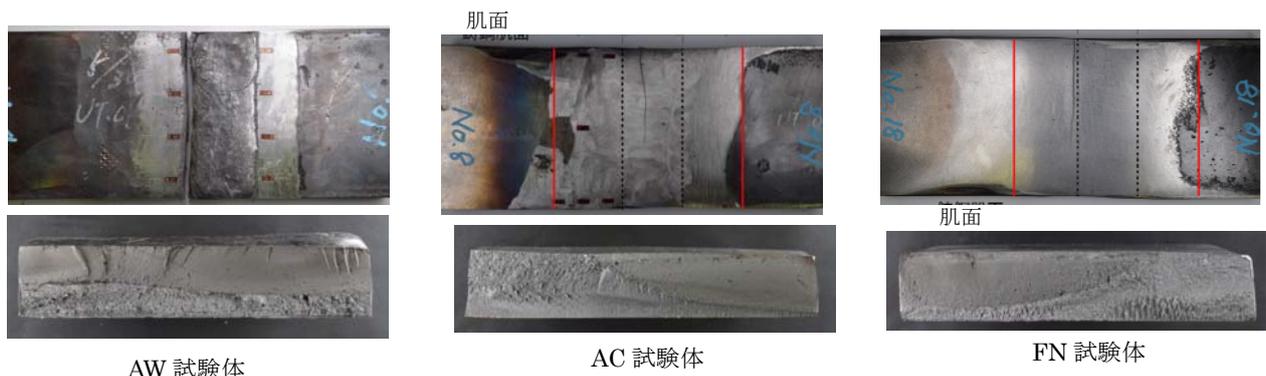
試験体下面の疲労き裂と疲労破面の例
